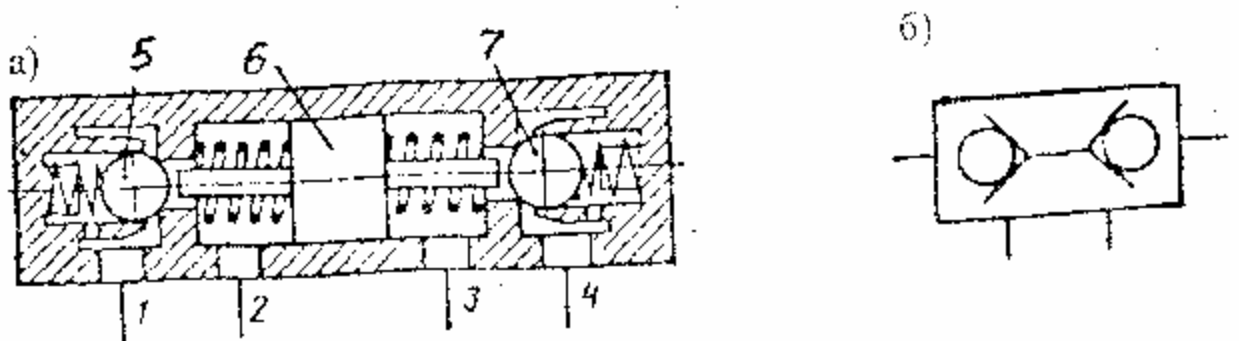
Двусторонний гидрозамок: а – конструктивная схема; б – условное обозначение
